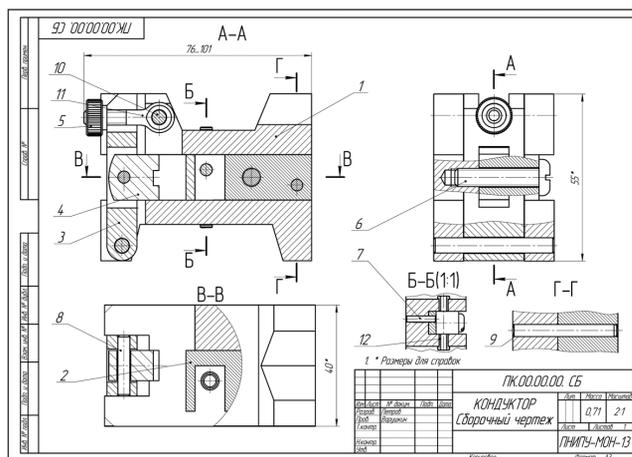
Ассоциативный сборочный чертеж кондуктора
